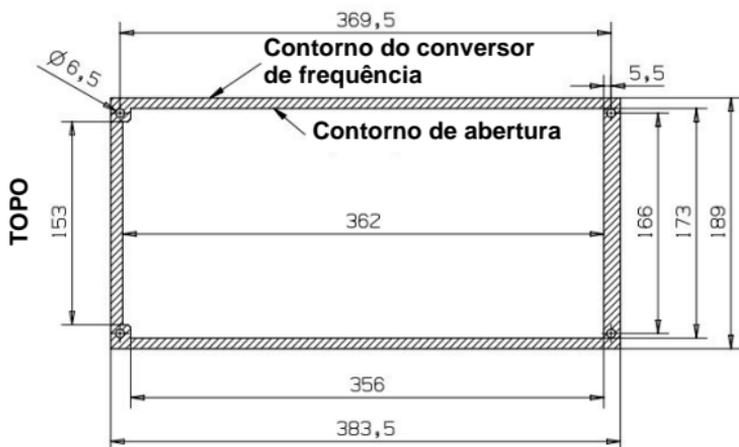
Dimensões do recorte para montagem em flange do M14
